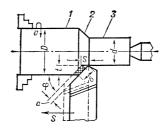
Элементы режима резания при гис. 1. Элеженты режима резания при точении: 1 — обрабатываемая поверхность; 2 — поверхность резания; 3 — обработанная поверхность: D — диаметр обрабатываемой заготовки; d — диаметр детали после обработки; a и b — толщина и ширина срезаемого слоя.
